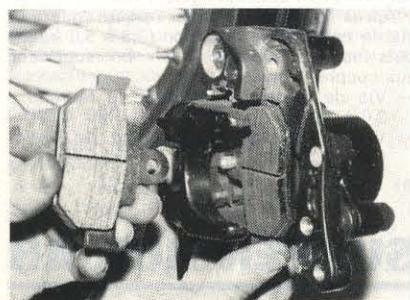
Dépose des plaquettes (Photo RMT)
